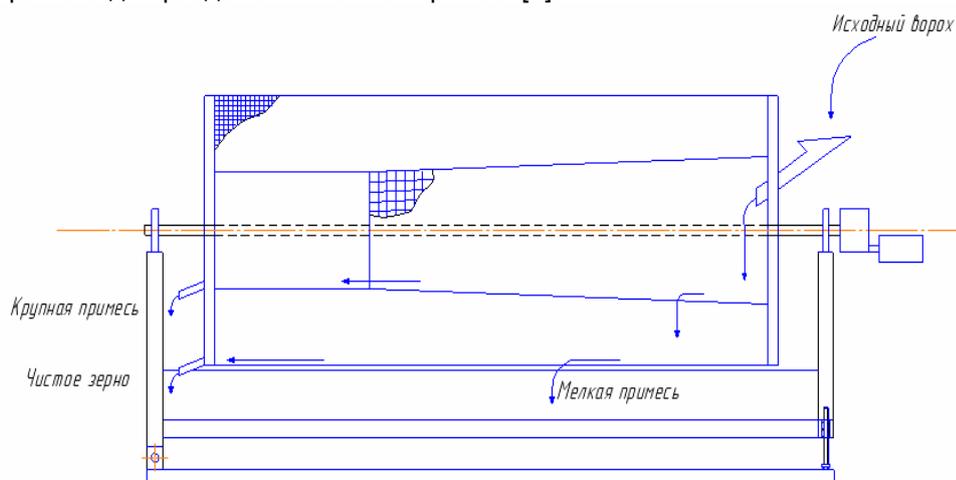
Конструктивно-технологическая схема со сдвоенными цилиндрическими решетами
